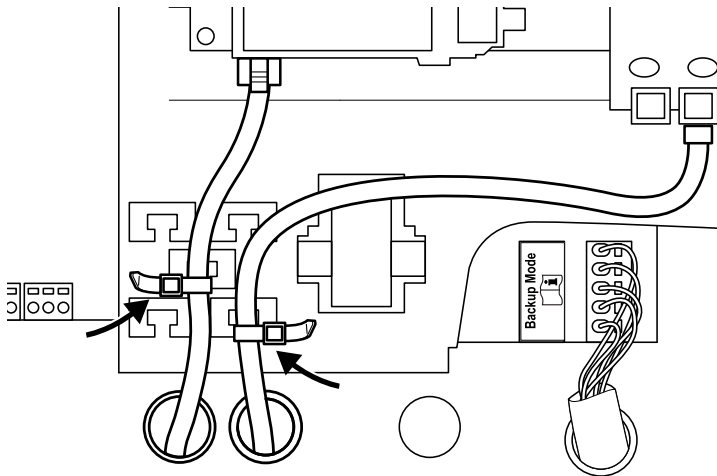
Kabel auf der Kabelaufgabe befestigen
